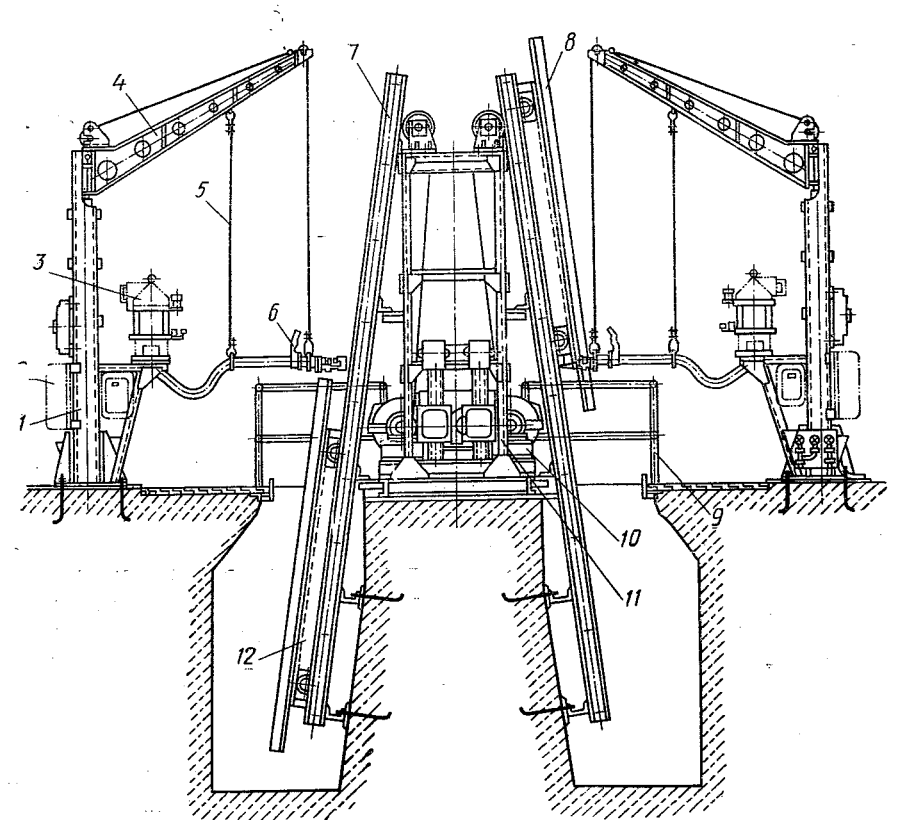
Двусторонняя вертикальная установка для сварки пространственных каркасов:
